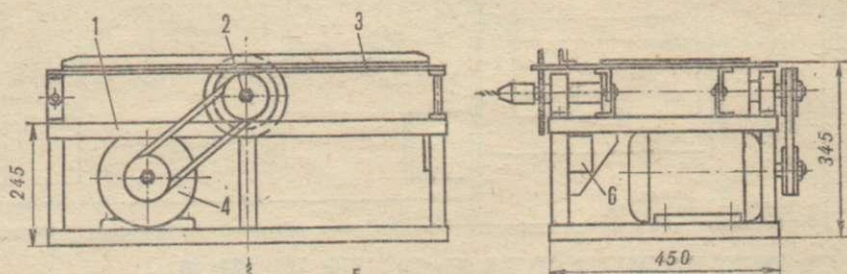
Устройство станка: 1 — станина, 2 — рабочий вал, 3 — стол, 4 — электродвигатель, 5 — направляющая планка, 6 — выключатель.
